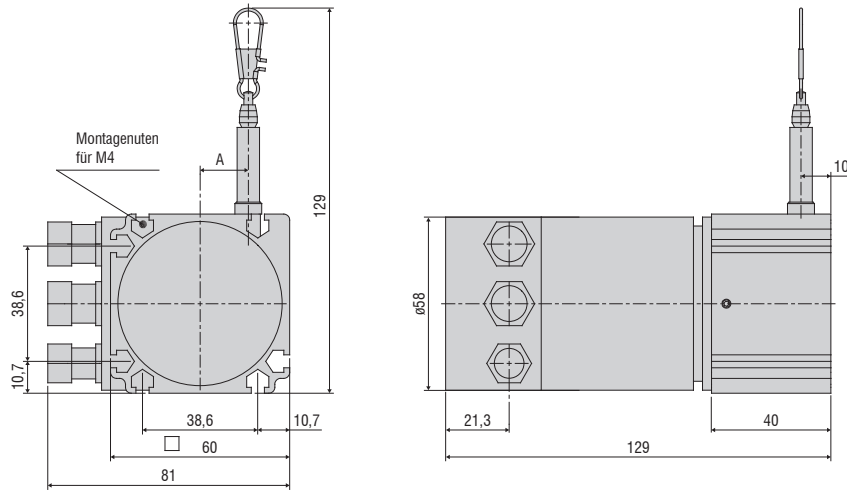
Maßzeichnung WDS- ... - P60 - BH - CO/PB/PN/ENIP/CAT, Abmessungen in mm
